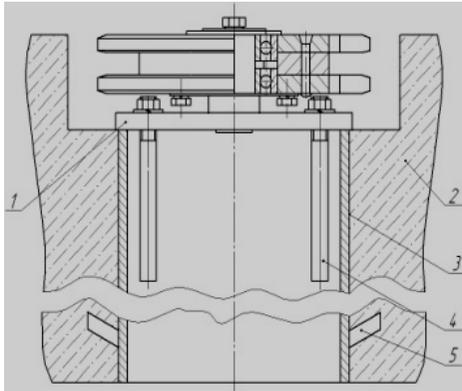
Схема крепления поворотного блока транспортера:
